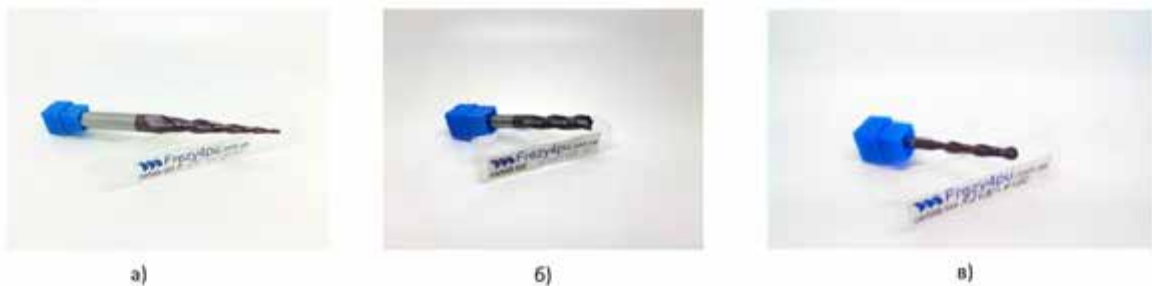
Інструмент для обробки дерев'яних заготовок: а) – конусна фреза; б) – кінцева фреза; в) – радіусна фреза.
